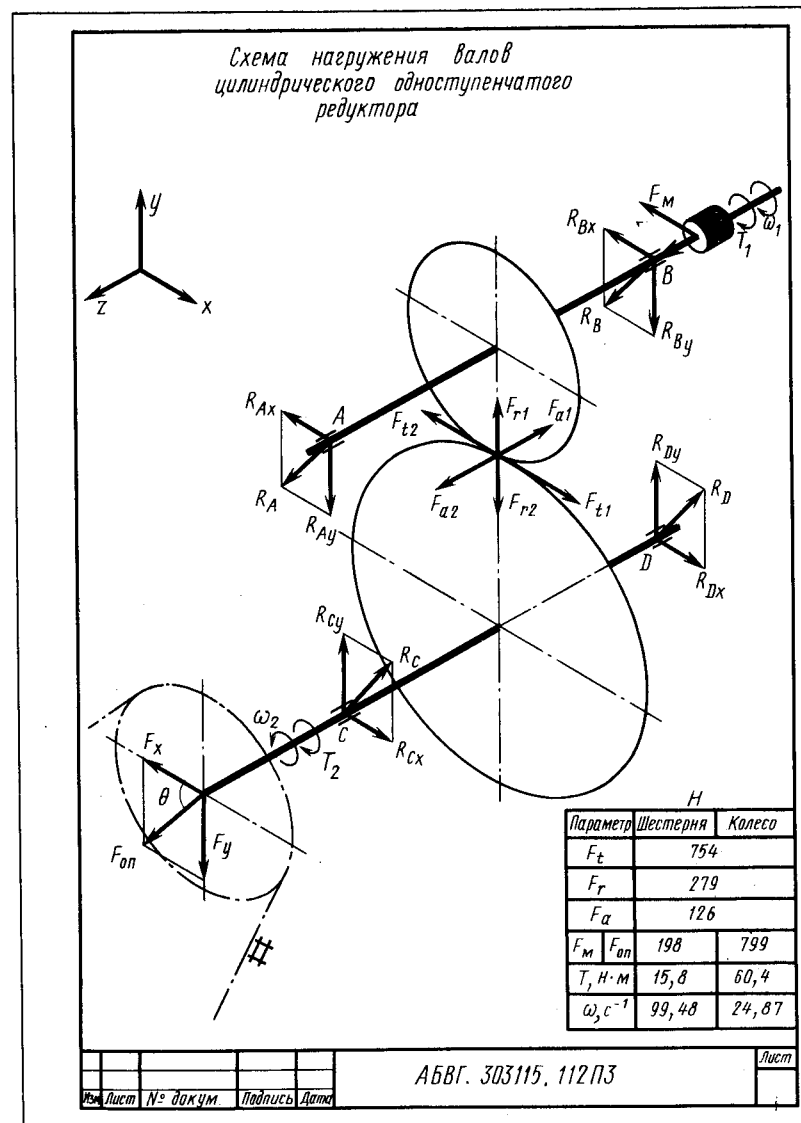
Пример схемы нагружения валов цилиндрического одноступенчатого редуктора
